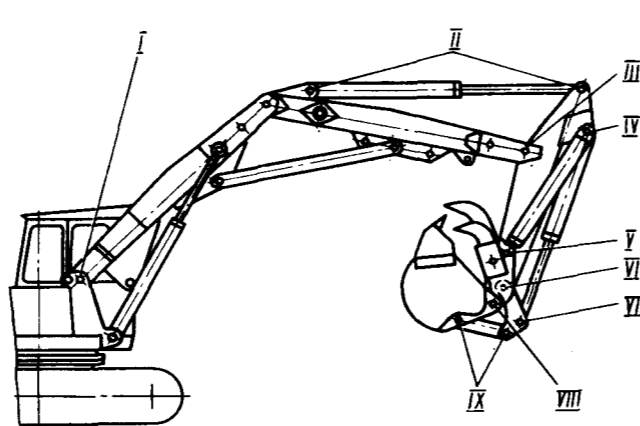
Схема смазки рабочего оборудования захватно-клевоего типа с трехзубым рыхлителем
